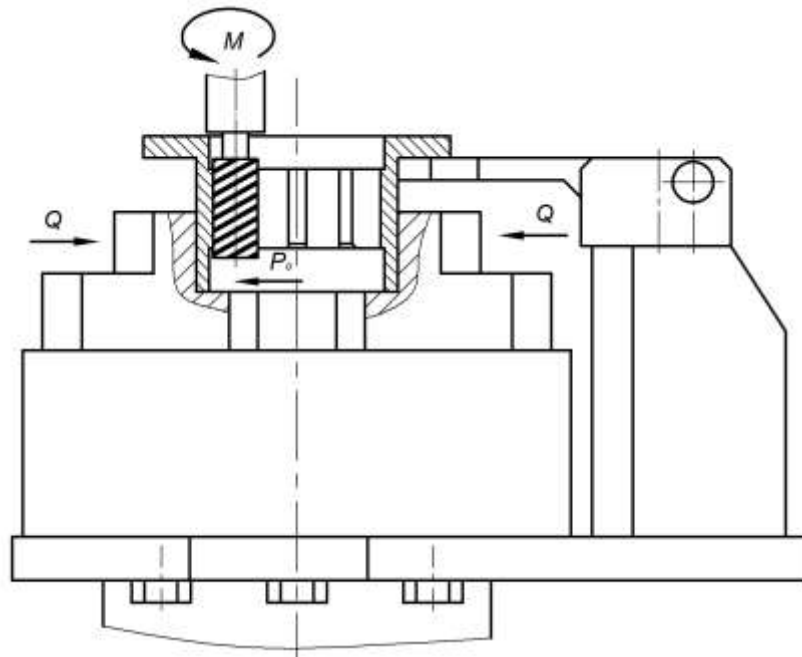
Схема базування та затиску деталі в пристрої для фрезерування шліців
